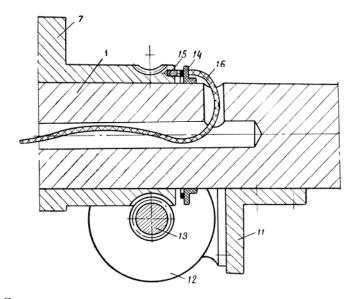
Схема размещения контактов, регистрирующих положение эксцентриковой втулки относительно оси: 1 — неподвижная ось; 7 — эксцентриковая втулка; 11 — кронштейн с закрепленным малогабаритным приводом; 12 — малогаборитный привод; 13 — червяк редуктора; 14 — электронепроводящее кольцо с наклеенным сопротивлением и контактом; 15 — контакт
